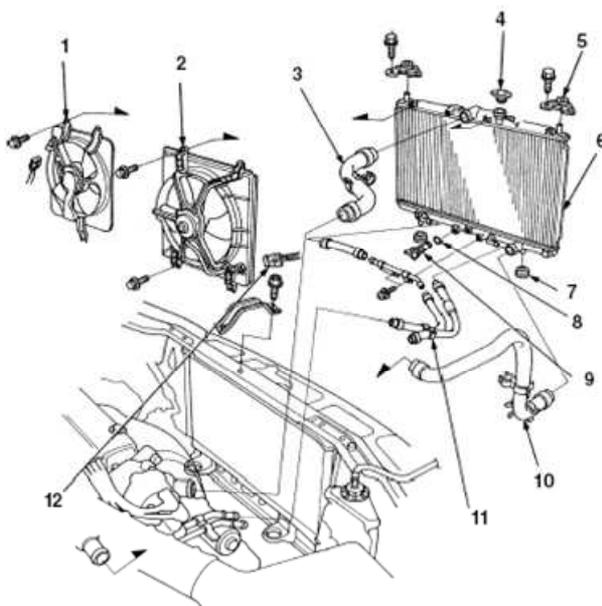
Монтаж элементов системы: 1 – защитный кожух вентилятора; 2 – направляющий кожух вентилятора; 3 – верхний патрубок радиатора; 4 – крышка радиатора; 5 – верхний кронштейн и подушка; 6 – радиатор; 7 – нижняя подушка; 8 – уплотнительное кольцо (заменить); 9 – сливной кран; 10 – нижний патрубок радиатора; 11 – патрубок охлаждения ATF; 12 – разъем мотора вентилятора
